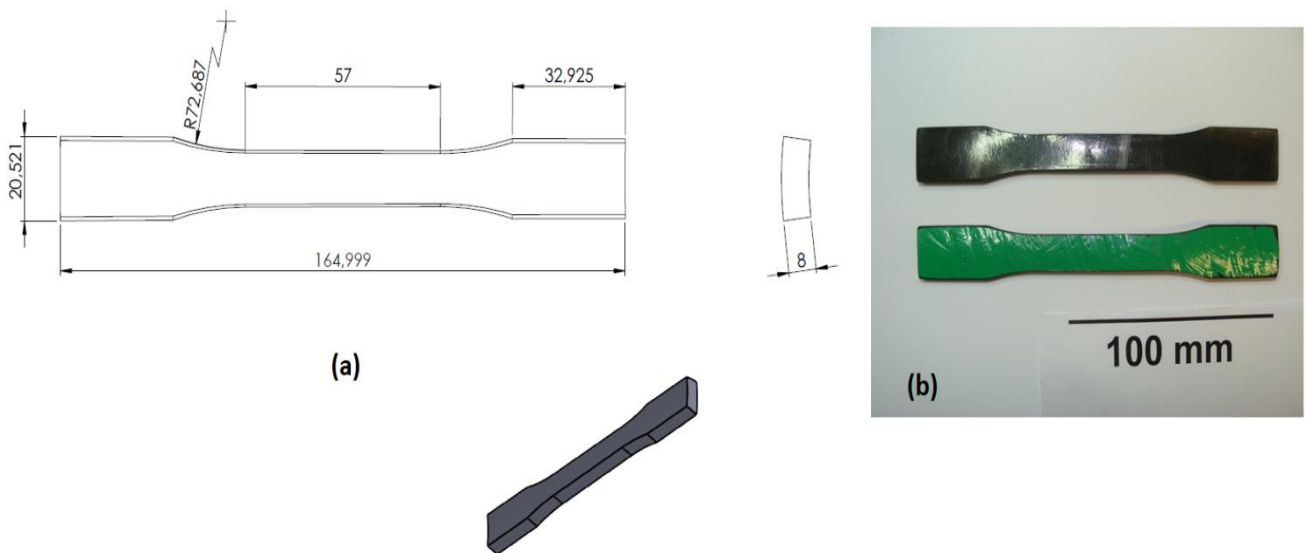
Corpo de Prova do Tipo III, (a) desenho com as dimensões do corpo de prova e (b) vista superior.
